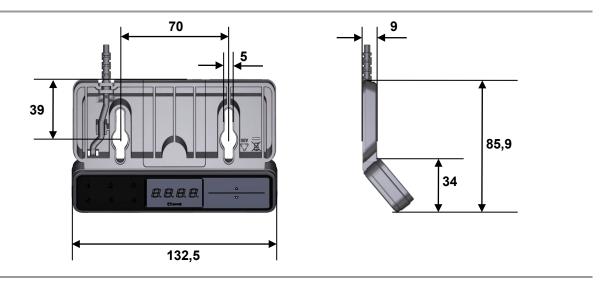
Bedienelement TOUCHfx, Montagemaße (Angaben in mm)
